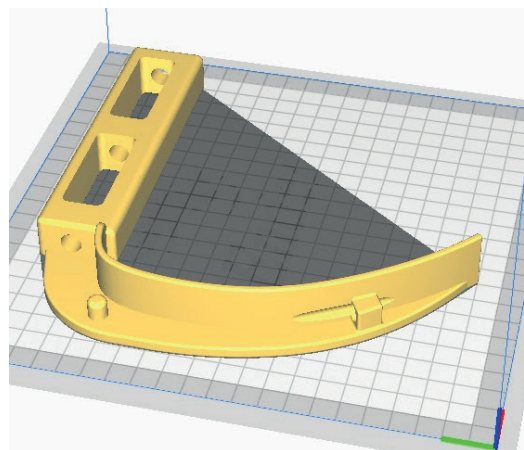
Diseño final de impresión de laringoscopio en ultimaker cura.
